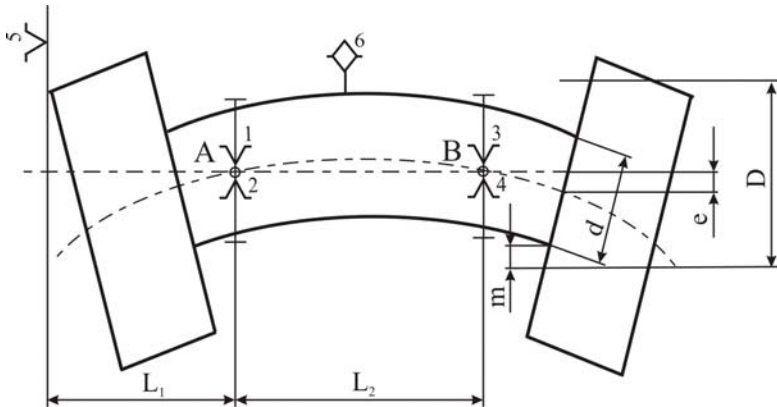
Схема расчета минимального выступа обработанной цилиндрической поверхности над телом детали.
